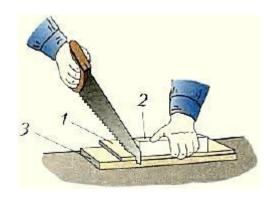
Пиление на подкладной доске: 1 — заготовка; брусок; 3 — подкладная доска
